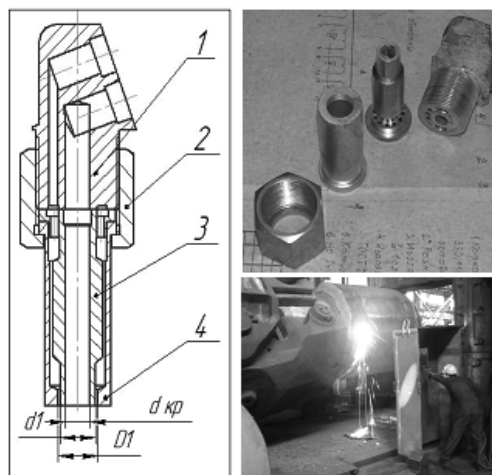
Модуль 6.6. Головка в сборе резака РПКЗ для выплавки дефектов на поковках – слева; детали модуля – справа сверху; процесс выплавки дефектов на поковке под прессом усилием 10000 тс – справа внизу
